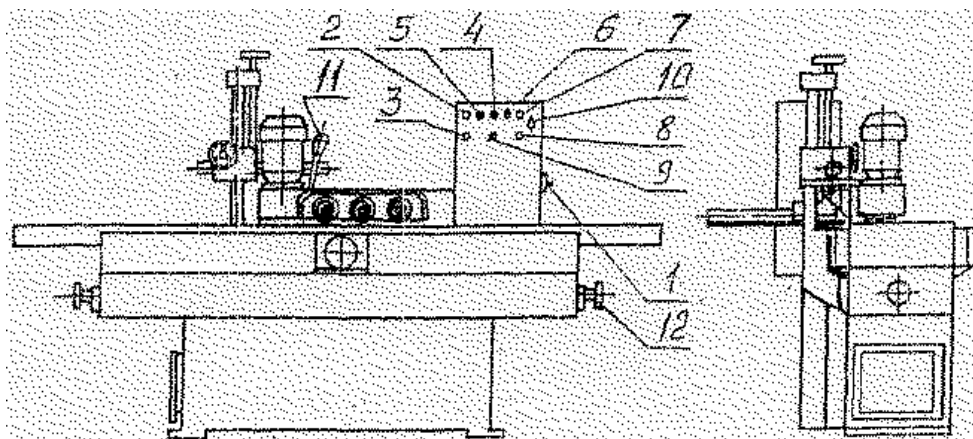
Общий вид станка СФ4А(К) с обозначением органов управления
